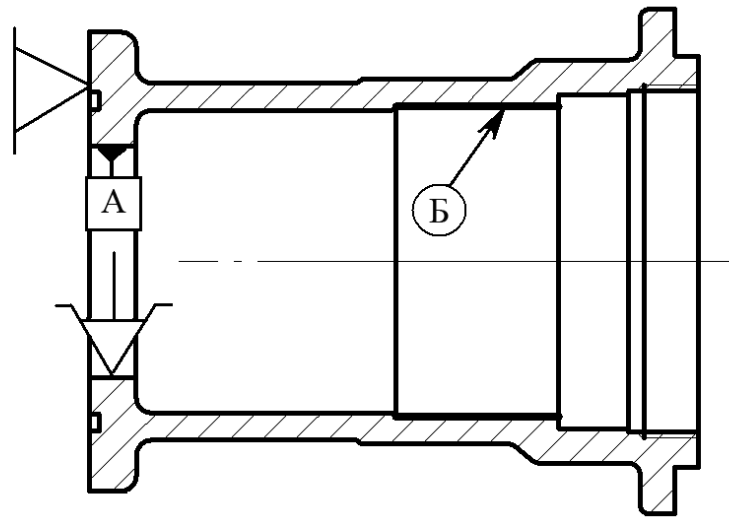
Схема закріплення деталі під час токарної обробки.
